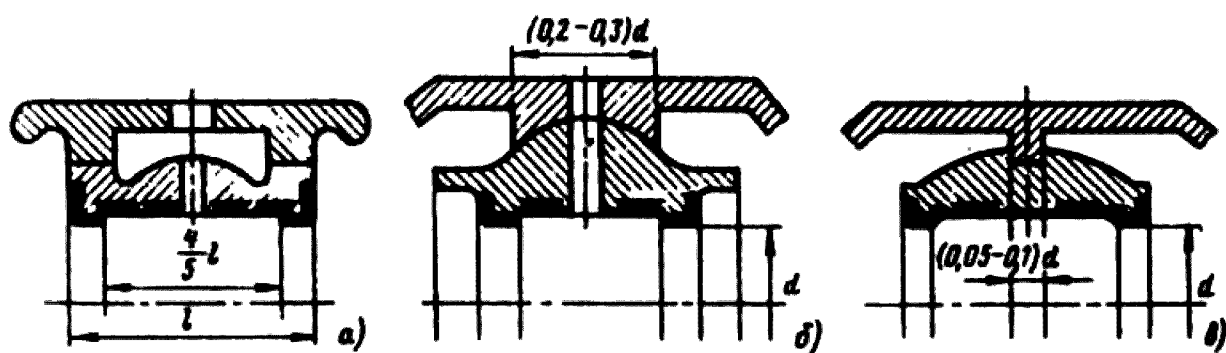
Посадки вкладышей в корпусе подшипника:
